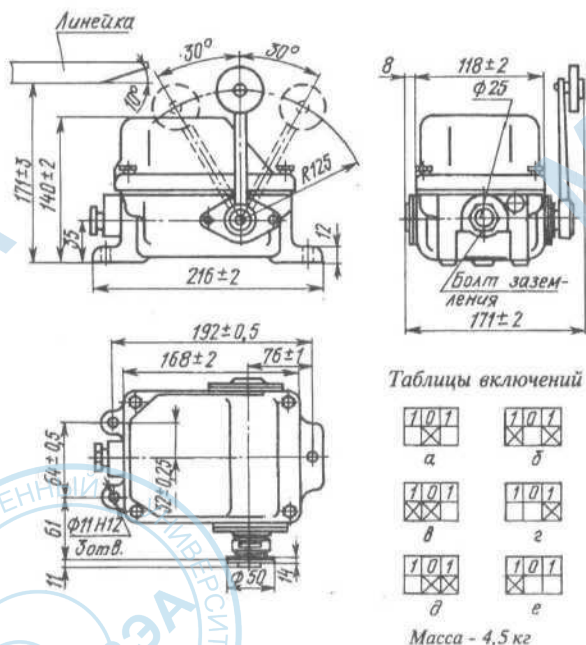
Габаритные, установочные размеры и масса выключателя типа КУ-741
